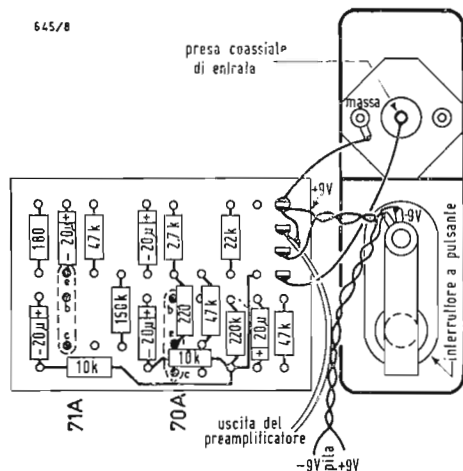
Disegno del cablaggio del preamplificatore microfonico equipaggiato con la piastrina 130. A destra: lato interno della parte superiore della scatola metallica che contiene tutti i componenti.
